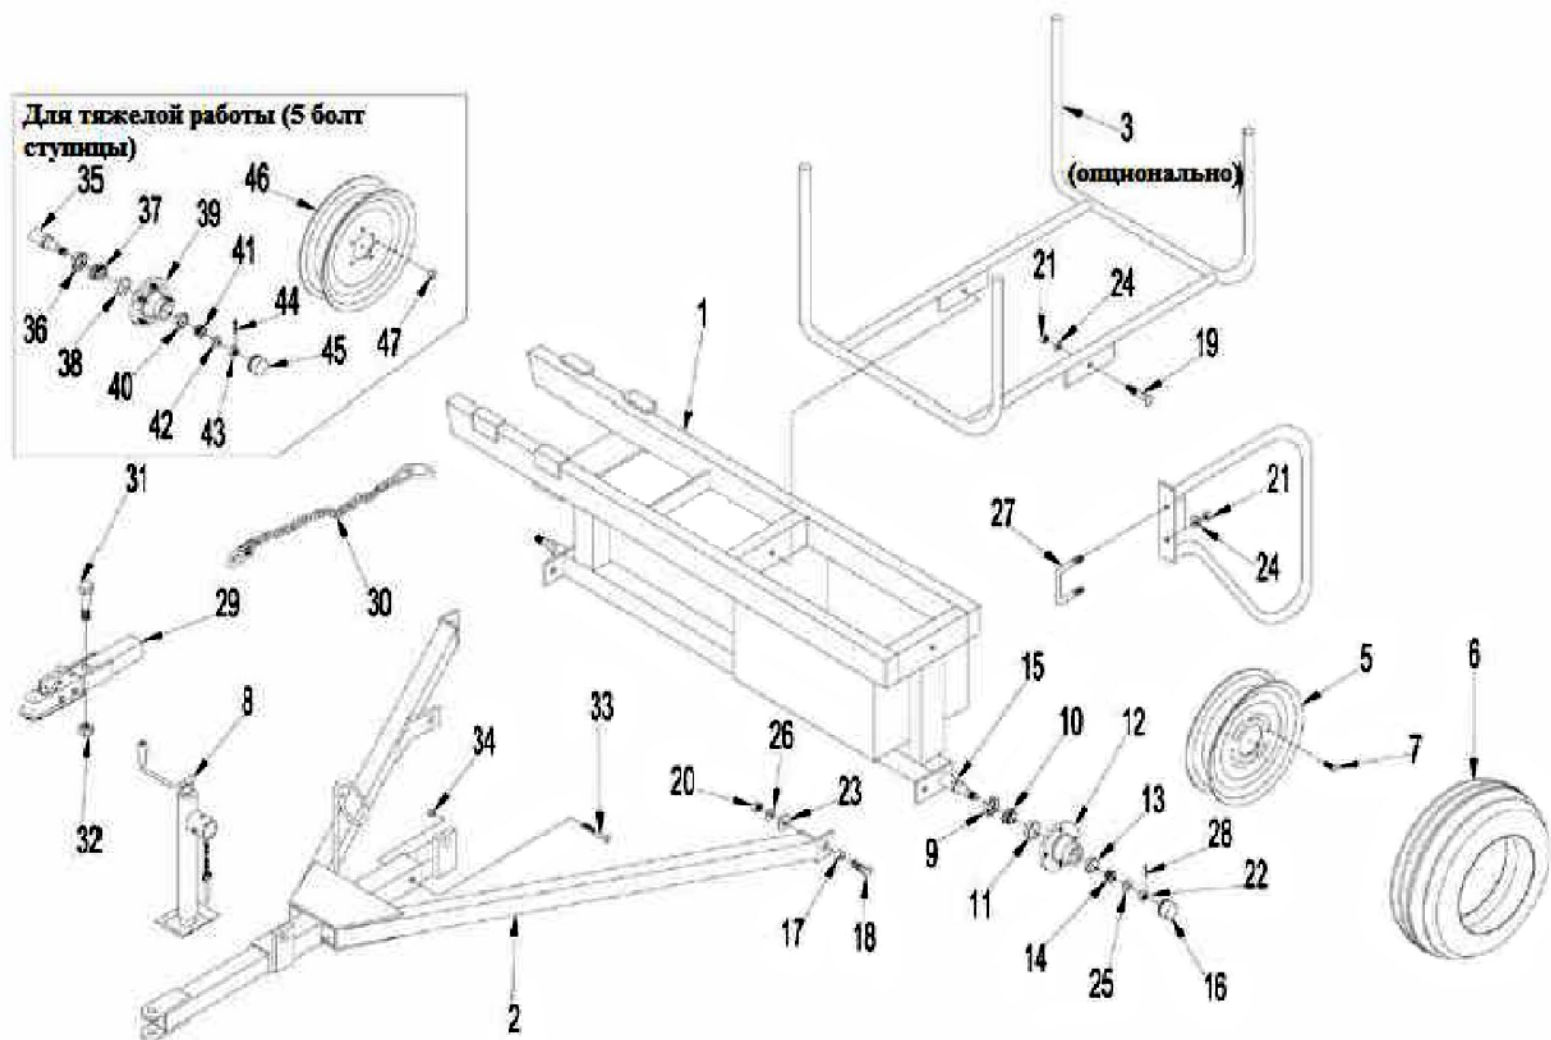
Рама и чертеж сцепного устройства в сборе
